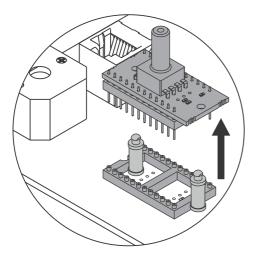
Извлечение пьезоэлектрического датчика из MSS PCB
